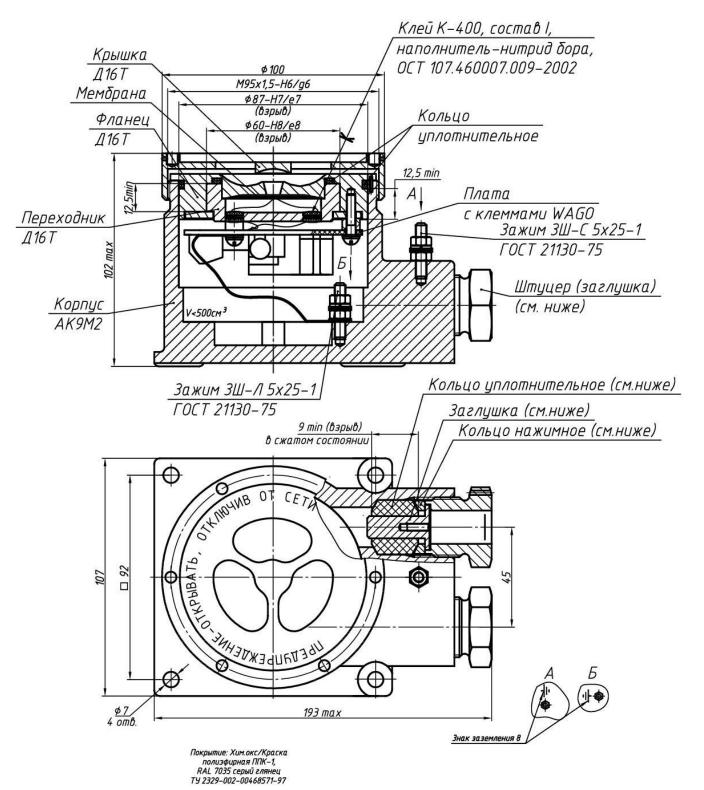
а - Габаритный чертёж звуковых оповещателей ЕхОППЗ-2B-A и ЕхОППЗ-2B-220-A в алюминиевом корпусе (вариант), совмещённый с чертежом взрывозащиты. Маркировка показана в п. 1.6.
